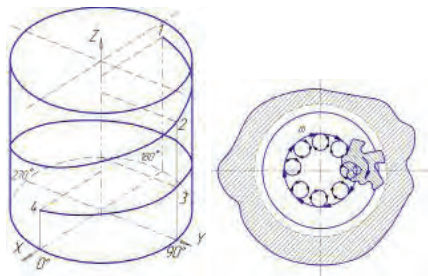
Схема трохойдного внутреннего резьбофрезерования
